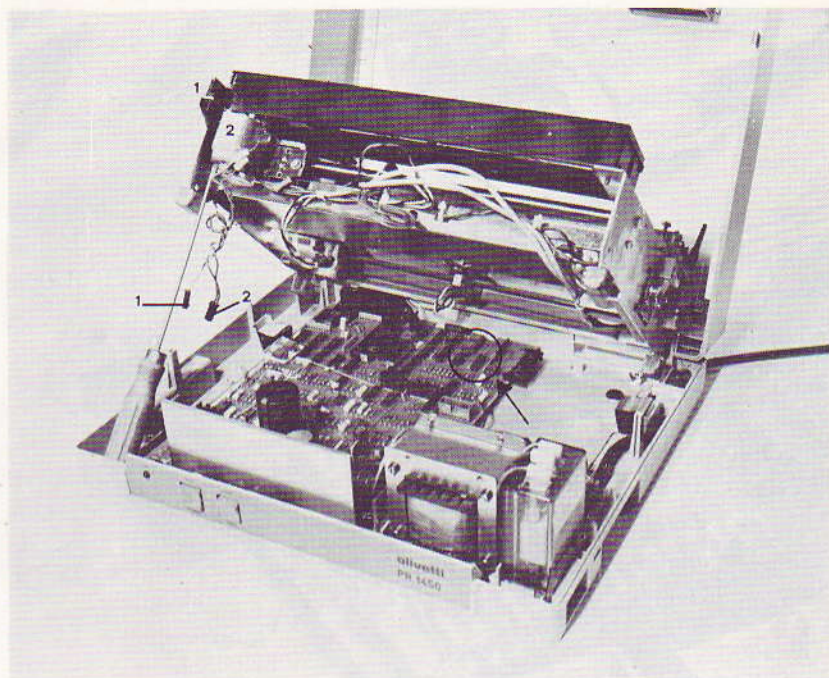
Localizzazione dip-switches PON Ø1-PON Ø2-PON Ø3.
